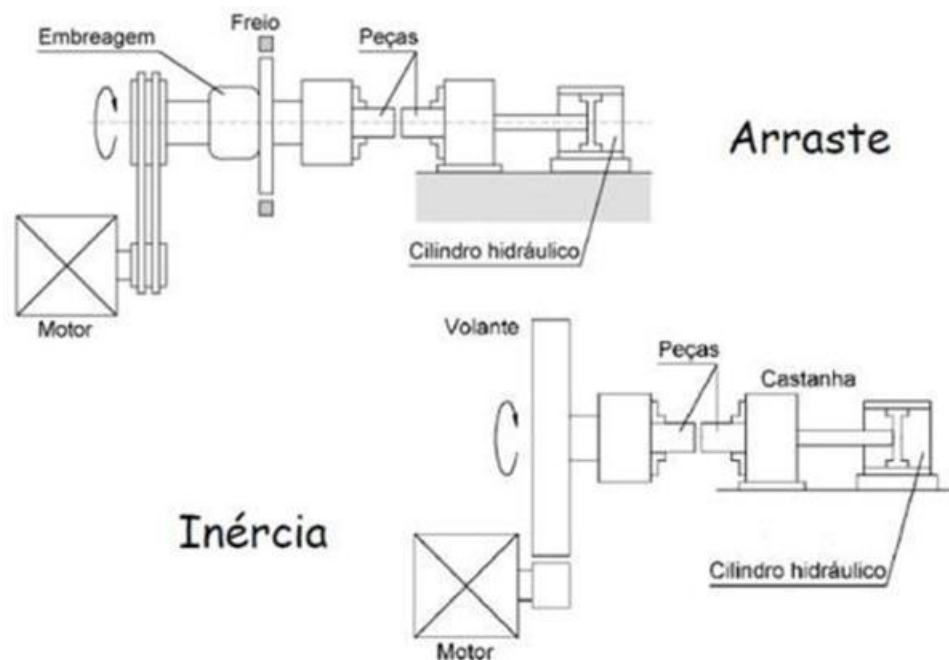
Equipamento Básico para Soldagem por Arraste e por Inércia
